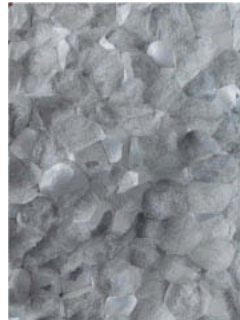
Der Bruch durch die Perle bezeugt die hohe Qualität der Verschweißung.
